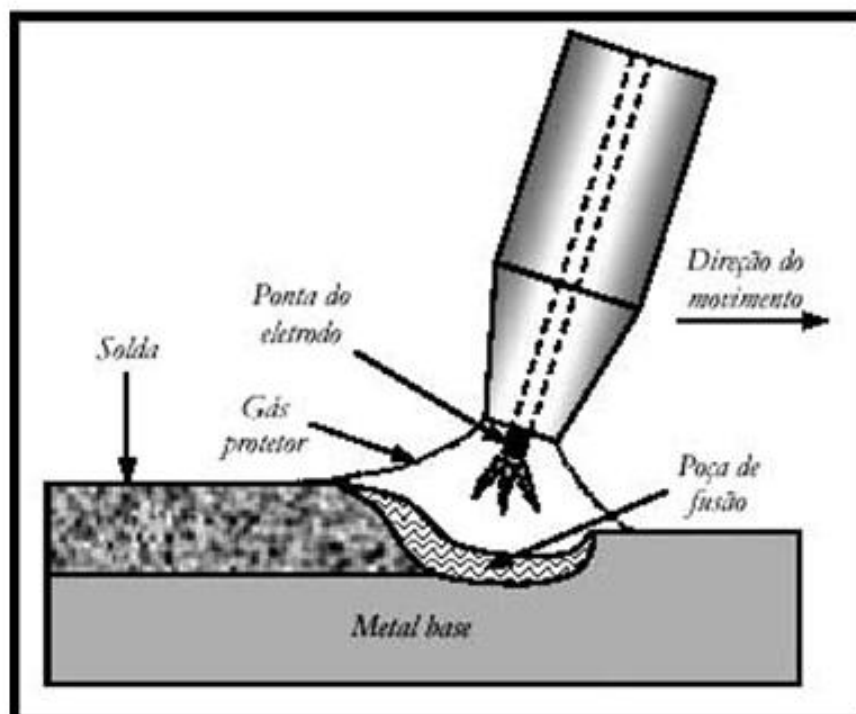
Representação esquemática do processo de soldagem MIG/MAG
